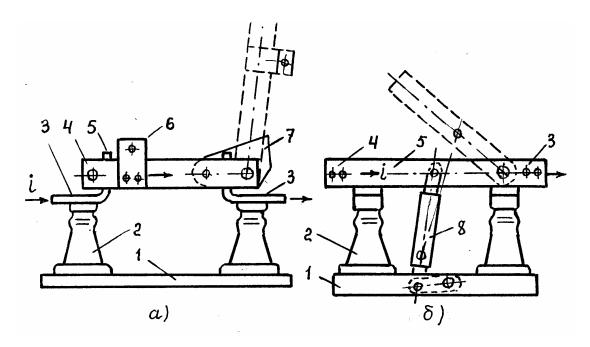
Конструктивные схемы разъединителей вертикально-поворотного типа: 1 — рама; 2 — опорный изолятор; 3 — вывод для присоединения подводящих проводов (шин); 4 — нож (подвижный контакт); 5 — неподвижный контакт; 6 — ушко для оперативной штанги; 7 — упор, ограничивающий поворот ножа; 8 — изоляционная тяга
